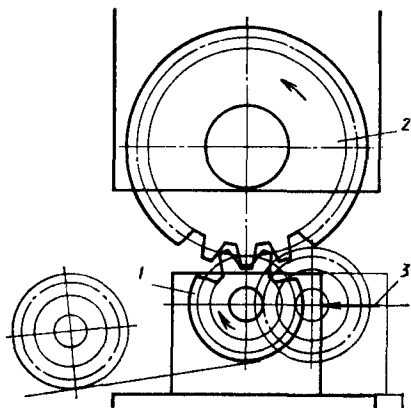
Схема зубокалибрования одним накатником с тангенциальным движением подачи заготовки:
